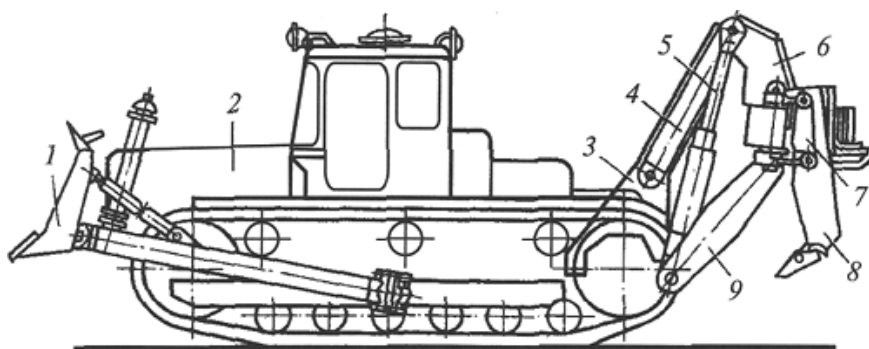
Бульдозер ДЗ-34С с рыхлительным оборудованием ДП-9С: 1 – бульдозерное оборудование; 2 – трактор; 3 – верхняя рама рыхлителя; 4 – верхняя тяга; 5 – гидродомкрат; 6 – балка; 7 – поворотное устройство; 8 – зуб; 9 – нижняя рама
